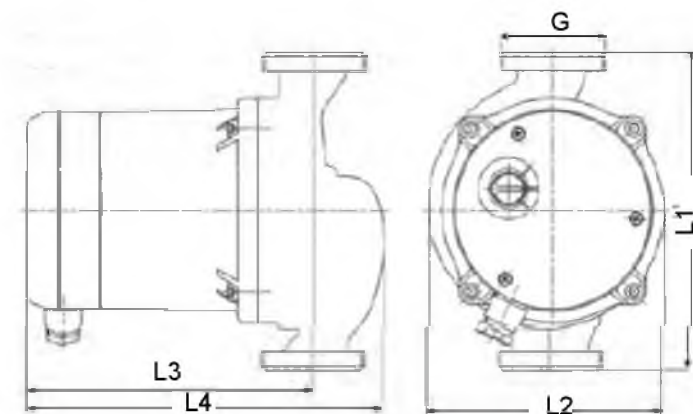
Габаритные размеры Calio-Therm NC 25-70
